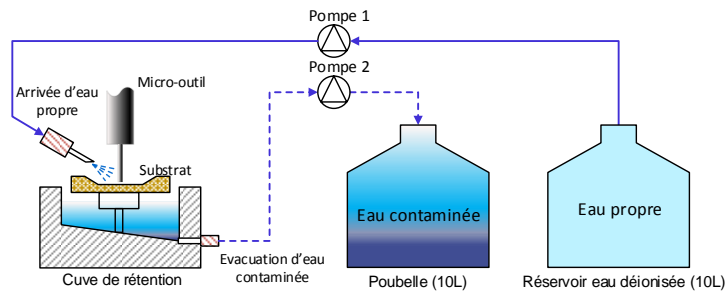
Circuit fluidique pour l'usinage par électroérosion.
